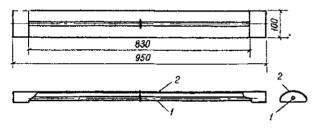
«Темный» излучатель излучающий стержень, 2 — рефлектор
